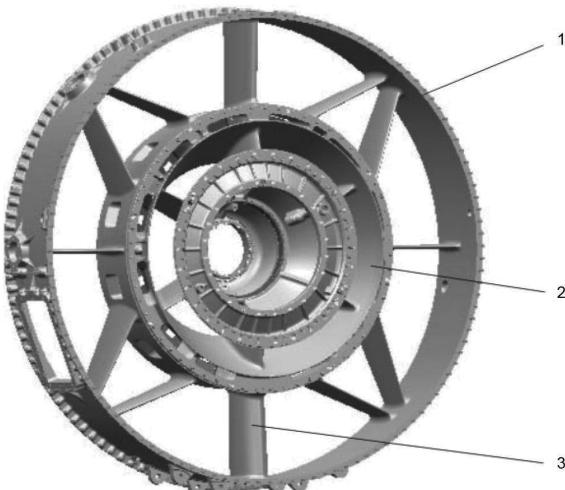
Основные элементы конструкции разделительного корпуса двигателя ПС-90А:
